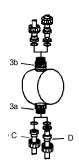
Raccordement de la conduite d'aspiration et de la conduite de refoulement
